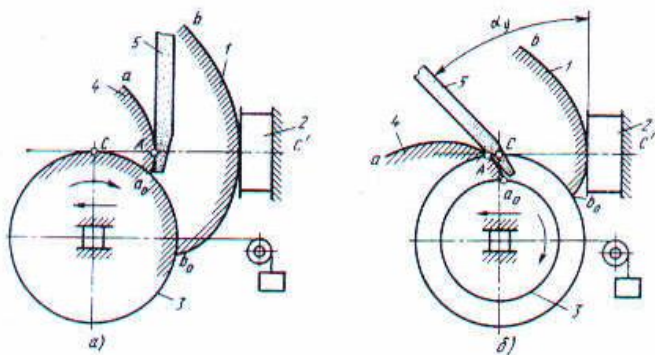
Шлифование эвольвентной поверхности долбяка плоской стороной дискового круга при использовании механизмов с эвольвентным кулачком:
